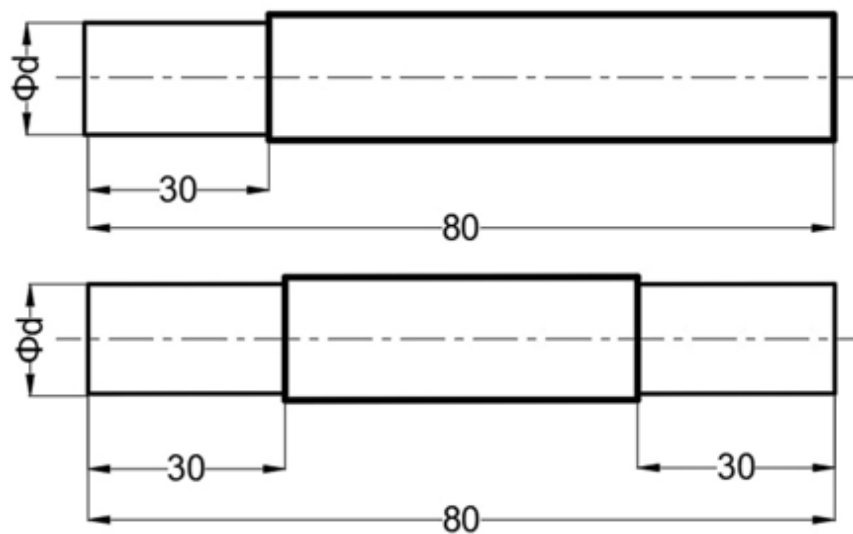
Dimensiones de las probetas para soldadura.
